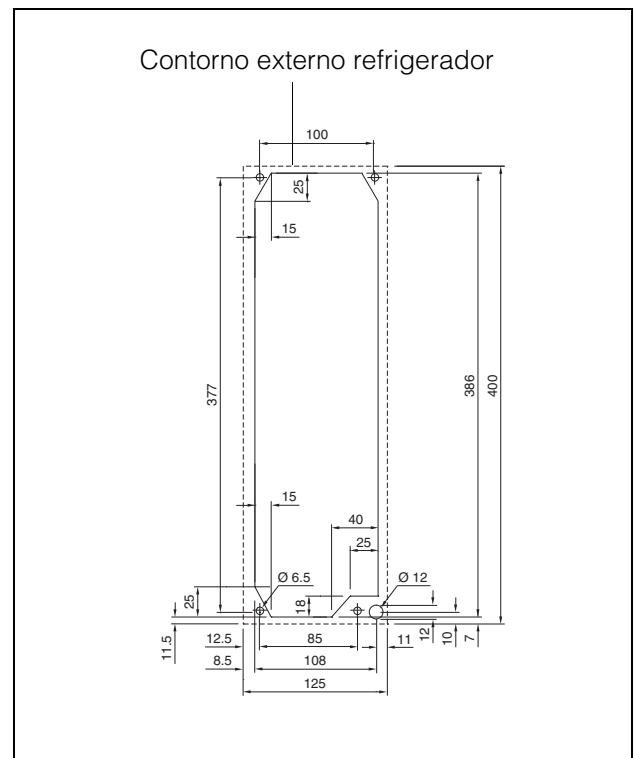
Escotadura de montaje y medidas de taladro con montaje interior del aparato (montaje completo)
